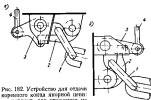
Устройство для очистки внутреннего звена якорной цепи: а — вариант для крепления на крышке ценового ящика; б — вариант для крепления на переборке.
